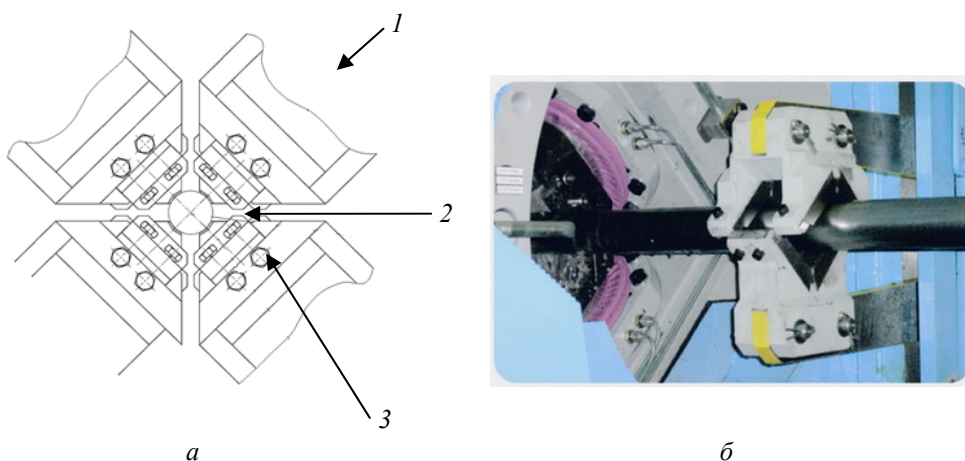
Радиально-ковочная машина: *а* – схематическое изображение; *б* – реальный вид; *1* – радиально-обжимная машина; *2* – заготовка; *3* – деформирующий инструмент
